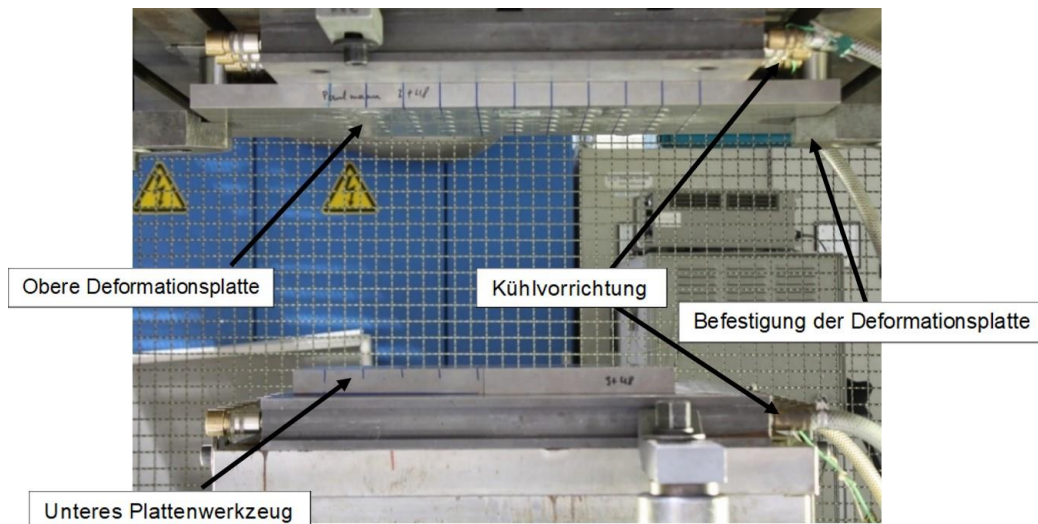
Im Pressenraum eingebaute Deformationsplatte mit Deformationselementen
